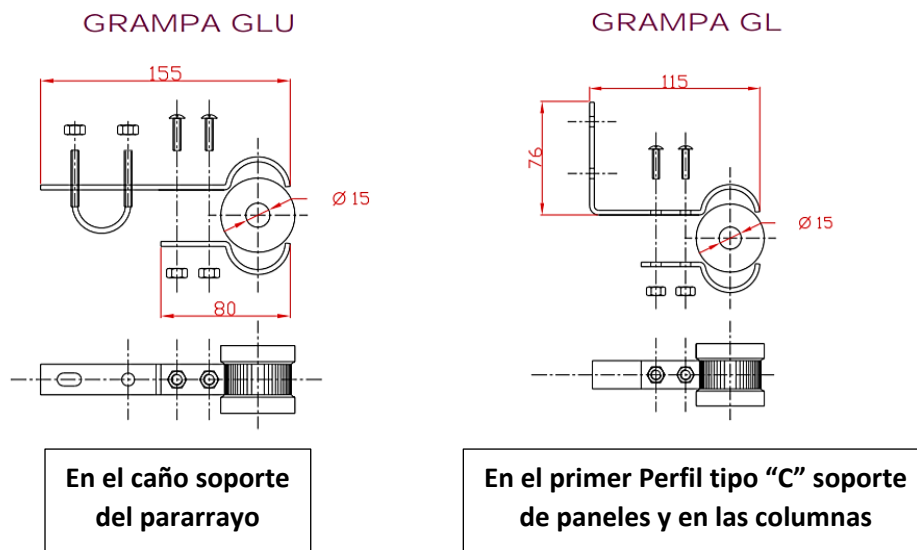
B: "Características de los soportes aislantes del conductor del SPCR" Fuente: GP (fabricante) [adaptación]
